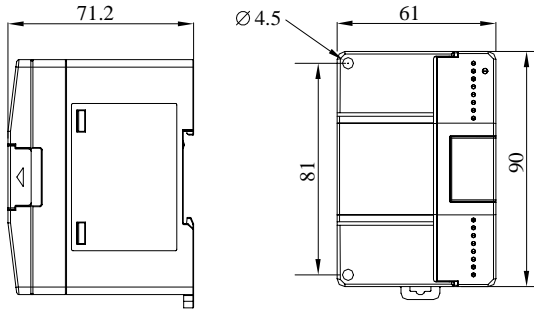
I/O 扩展模块外形尺寸与安装孔位尺寸
